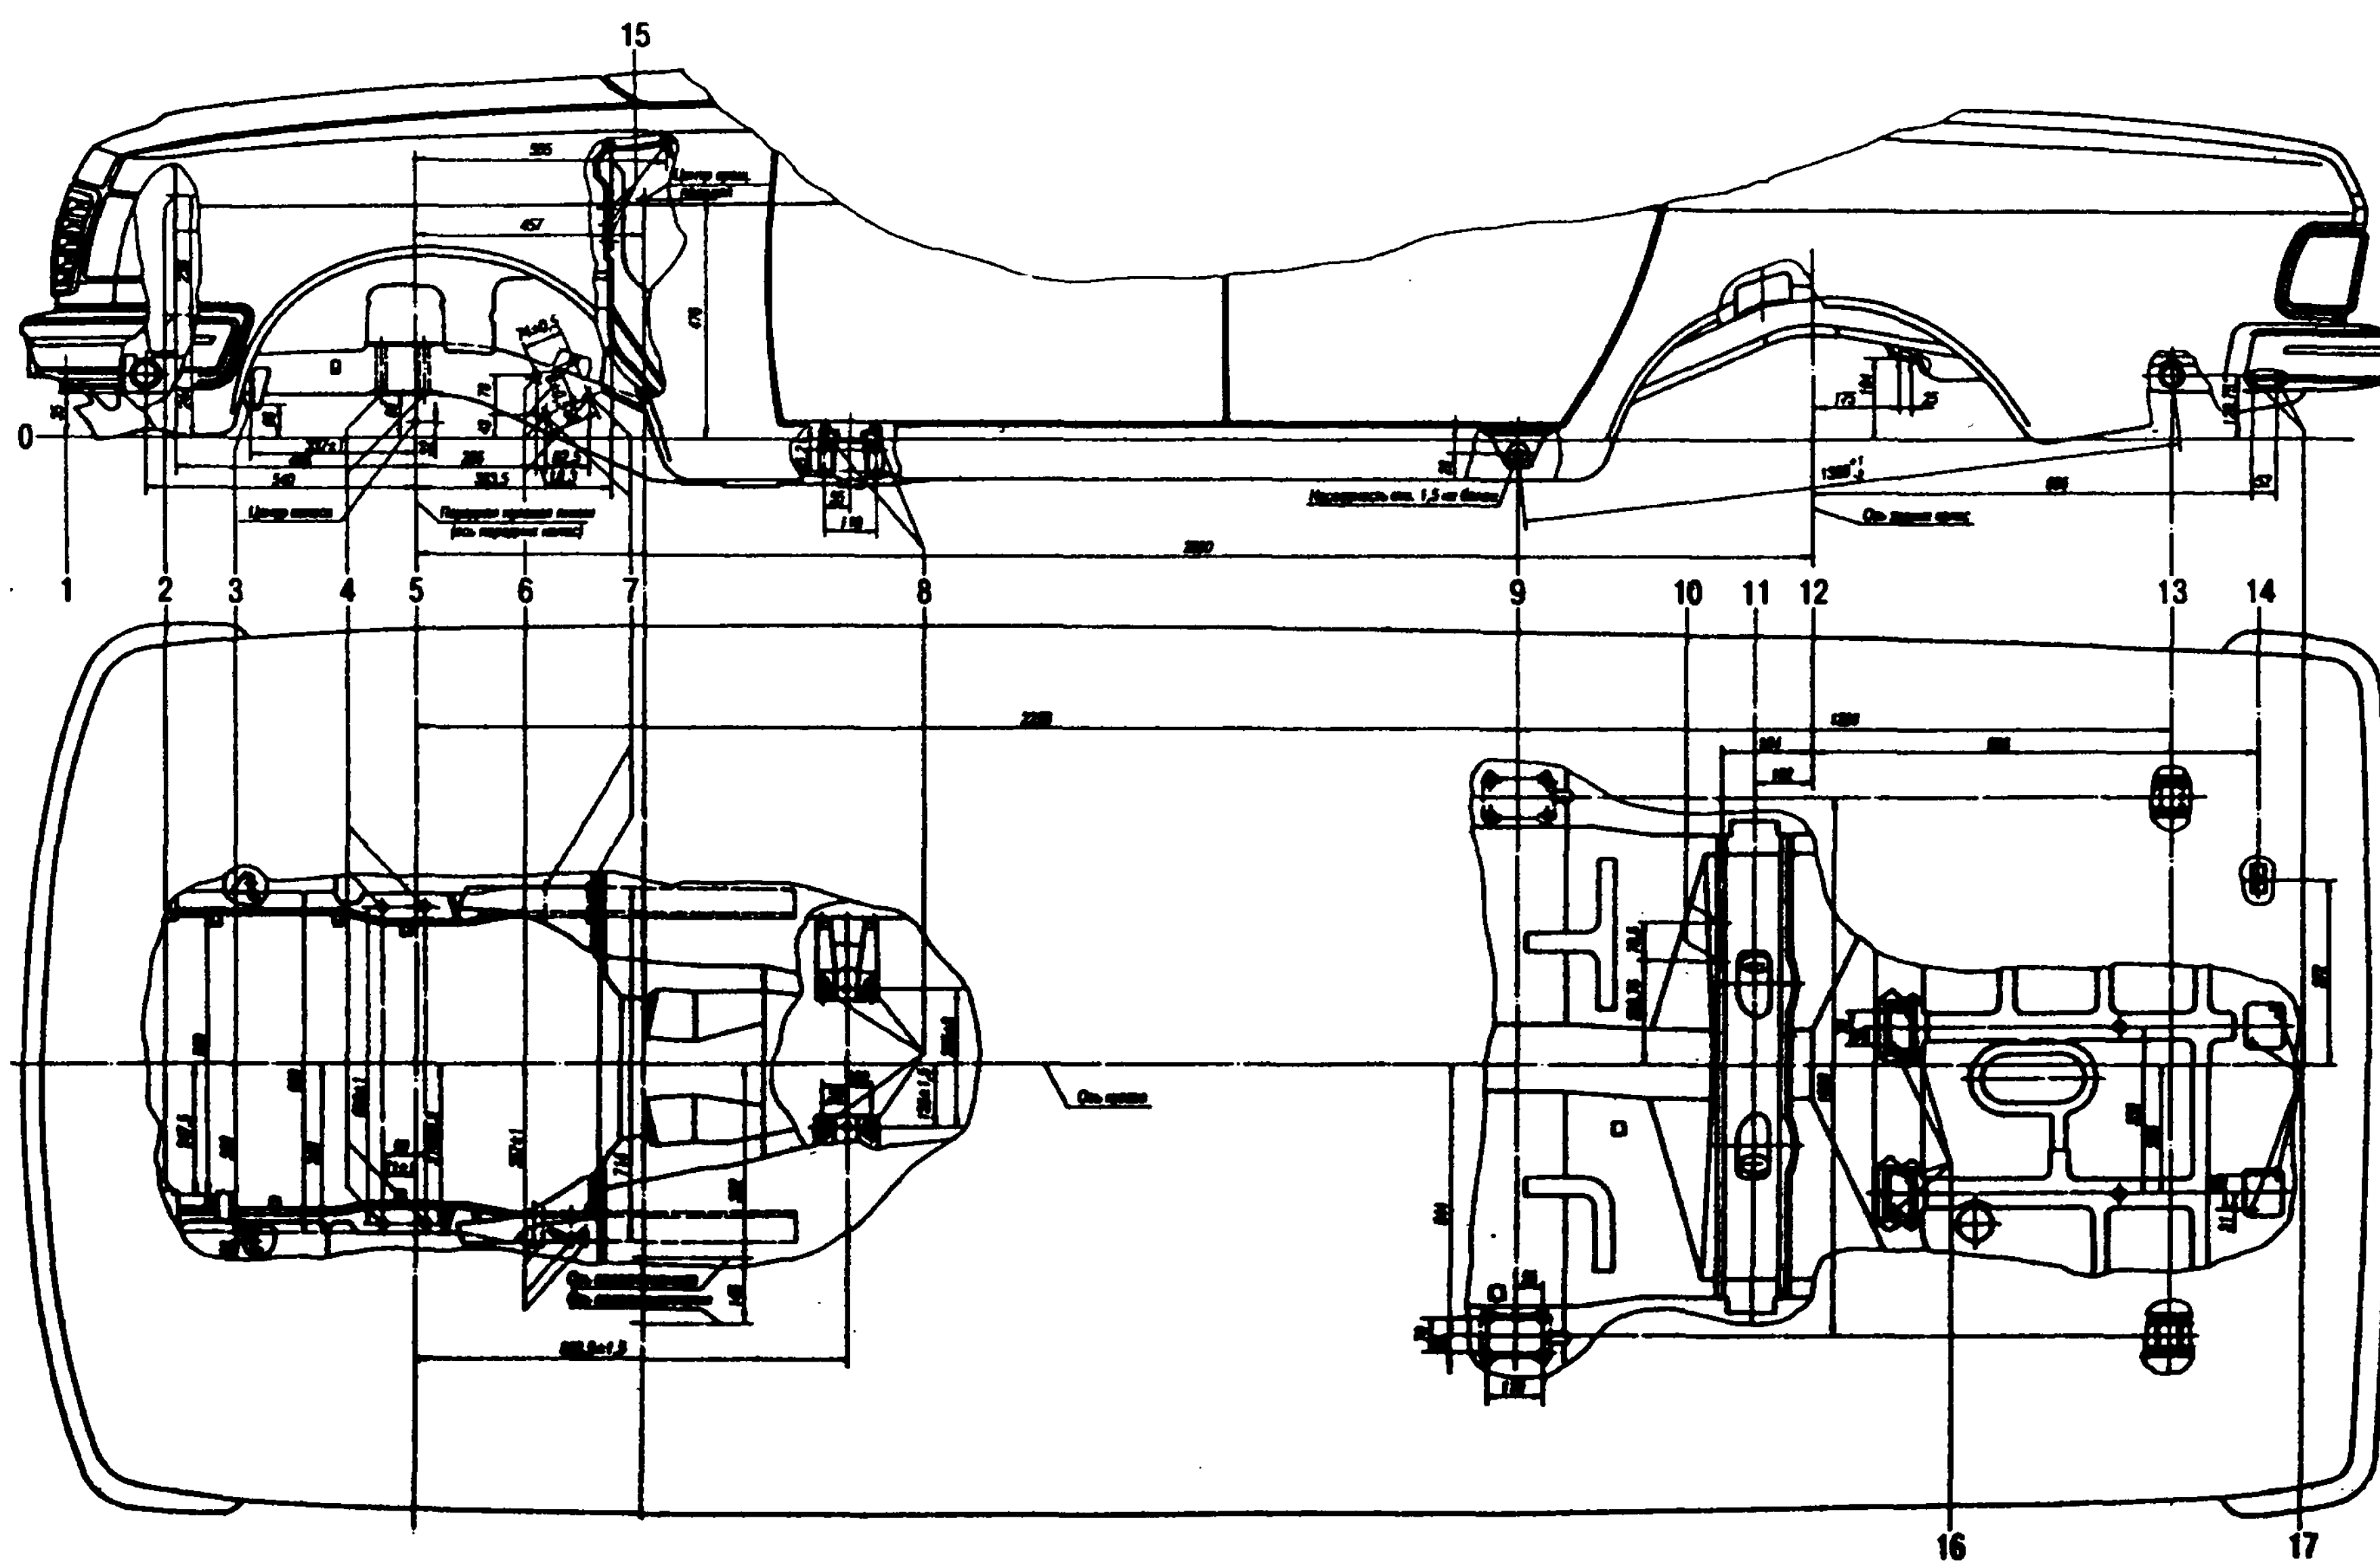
Контрольно-установочные размеры крепления агрегатов: 1 - базовая линия - нижняя нулевая; 2 - крепление радиатора; 3 - крепление стабилизатора поперечной устойчивости; 4 - крепление передней подвески; 5 - ось передних колес; 6 - крепление картера рулевого управления; 7 - крепление маятника рычага; 8 - заднее крепление силового агрегата; 9 - крепление переднего конца рессоры; 10 - переднее крепление рессоры; 11 - крепление амортизаторов; 12 - ось задних колес; 13 - крепление заднего конца рессоры; 14 - заднее крепление глушителя; 15 - крепление приводов тормоза и сцепления; 16, 17 - крепление бензобака
